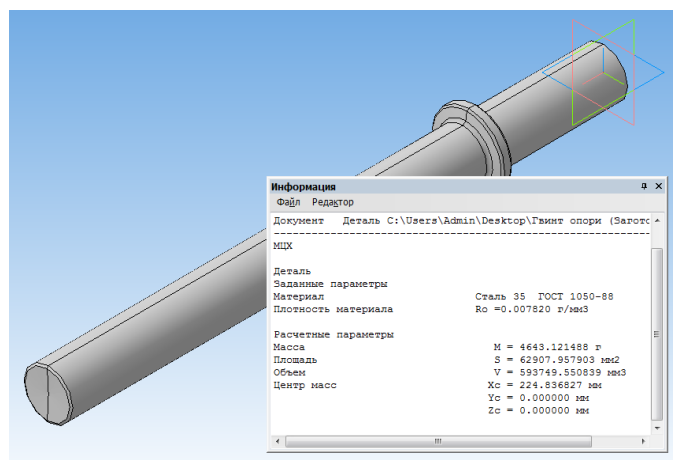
Модель та розрахунок штамповки заготовки «Гвинт опори»
